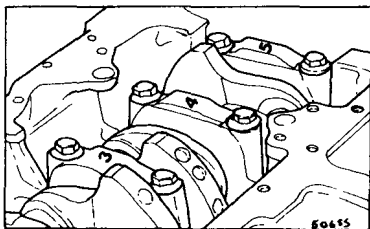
Установите крышки коренных подшипников с номерами 3,4 и 5
